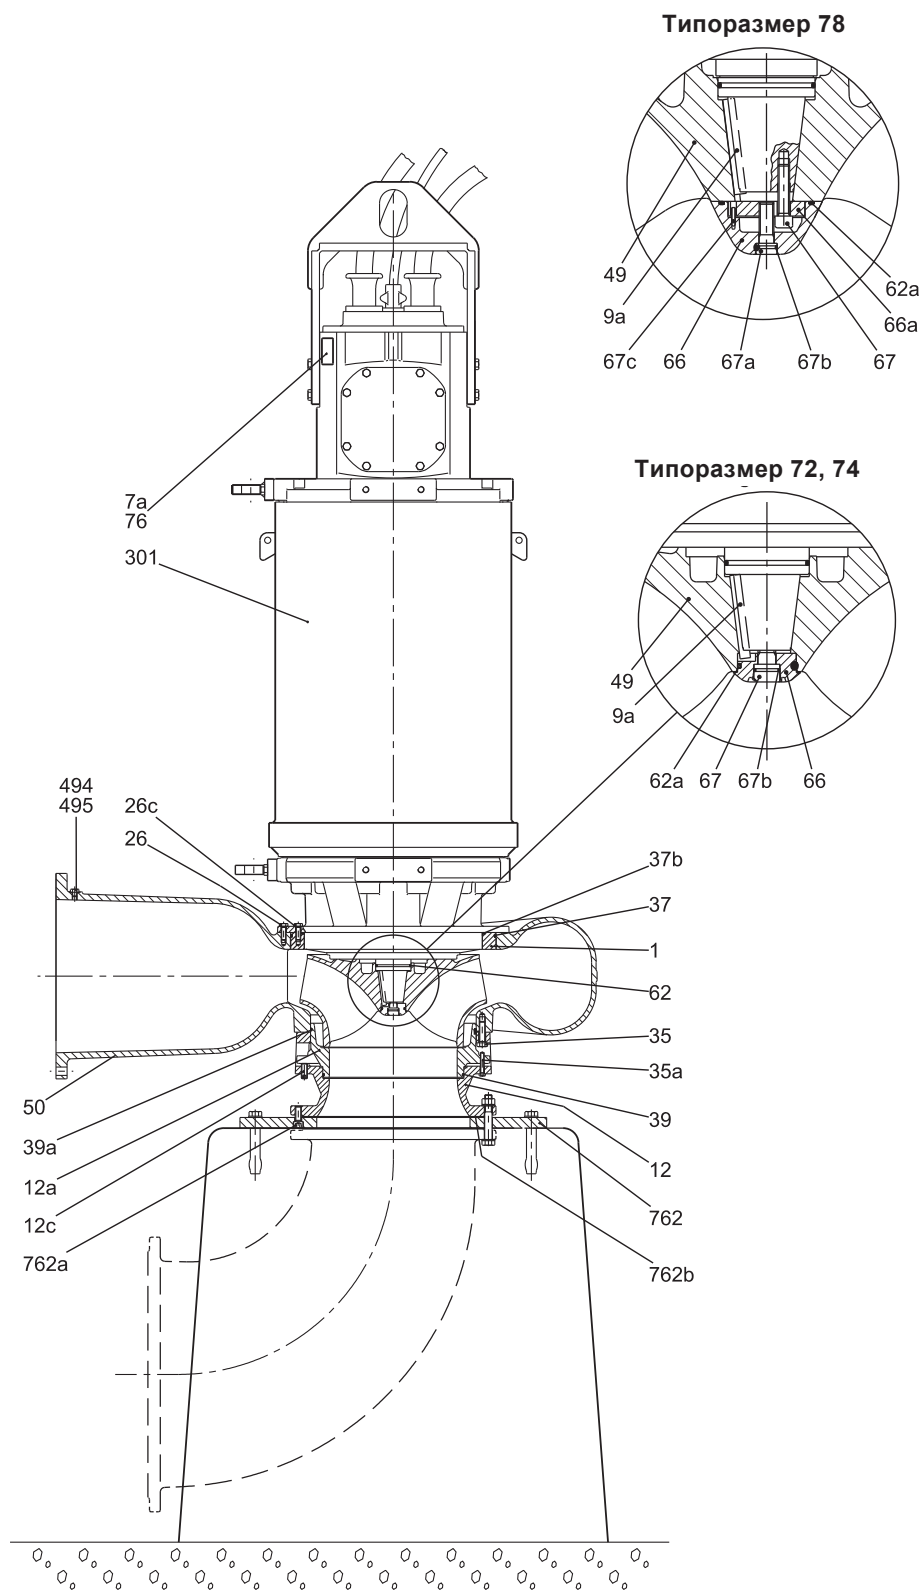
Тип установки D «сухая» вертикальная установка на плите-основании (бетонный фундамент).
